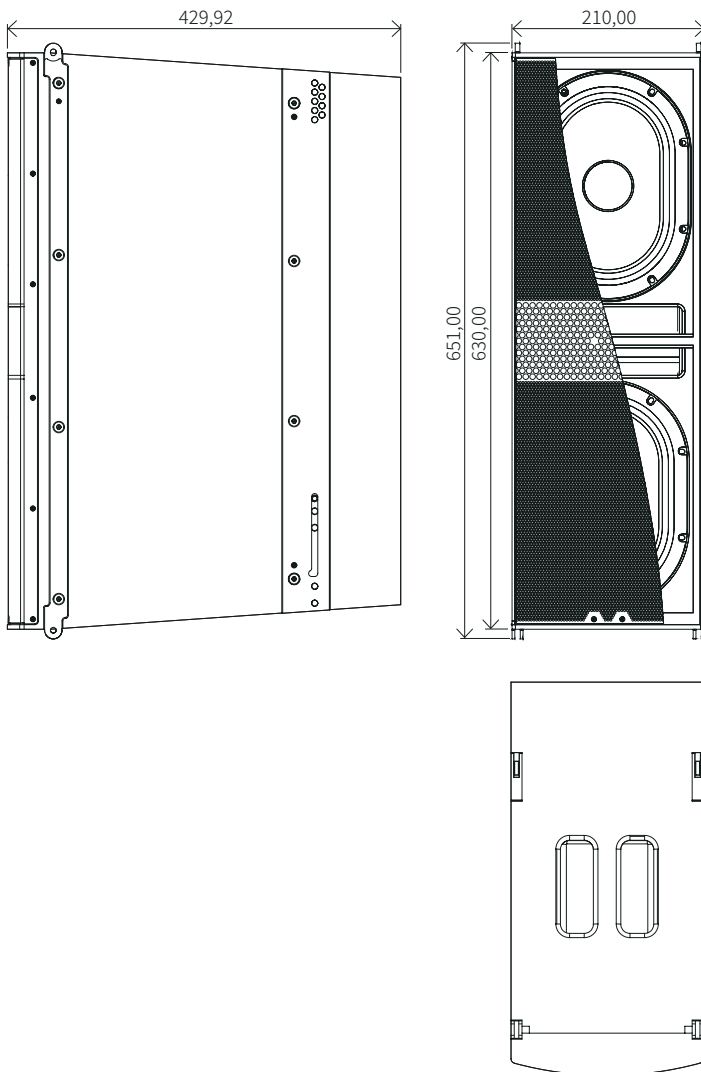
M-F3A FS Ansichten und Abmessungen. Bemaßung in Millimetern.
